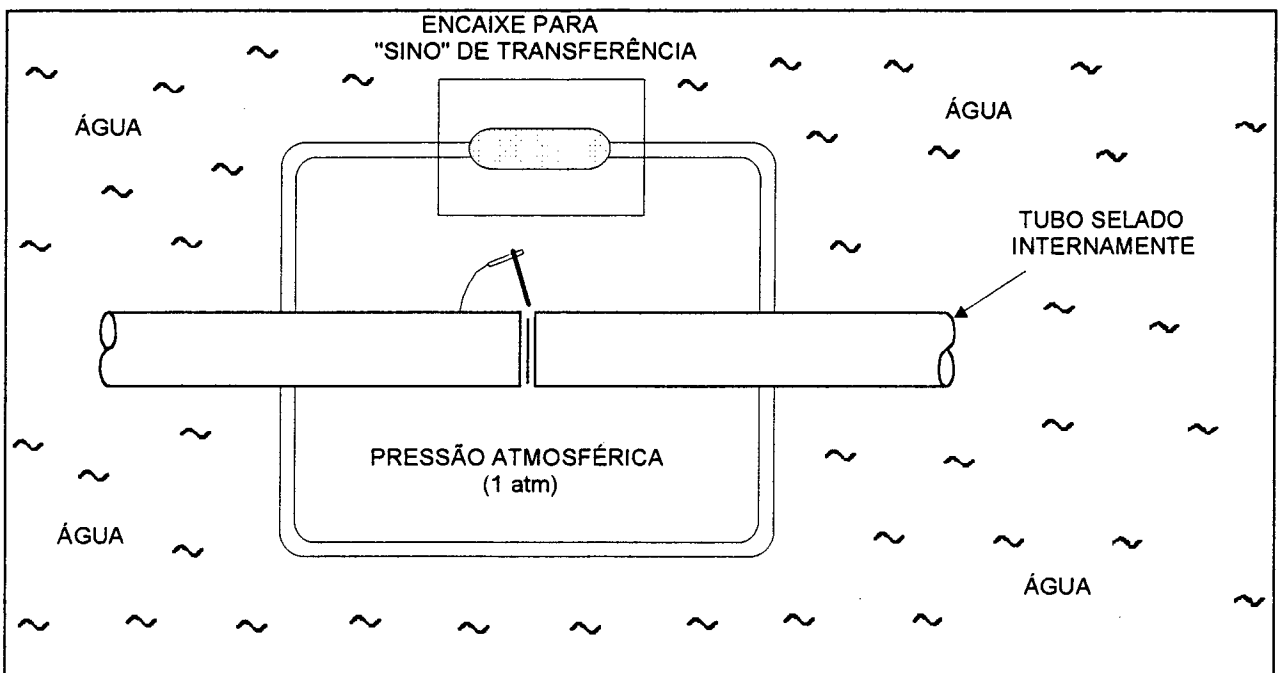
Técnica da soldagem subaquática a 1 (um) atmosfera [8].
